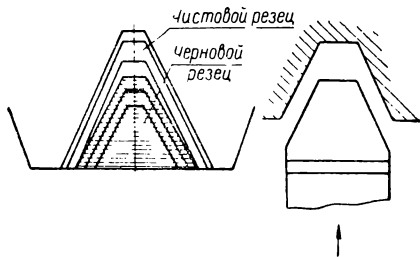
Геометрические параметры режущей части резьбового резца В. Бирюкова.
